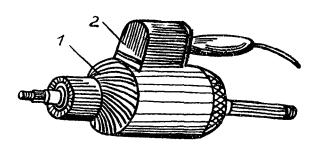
Проверка якоря на межвитковое замыкание: I — якорь генератора; 2 — портативный дефектоской ПДО-1
